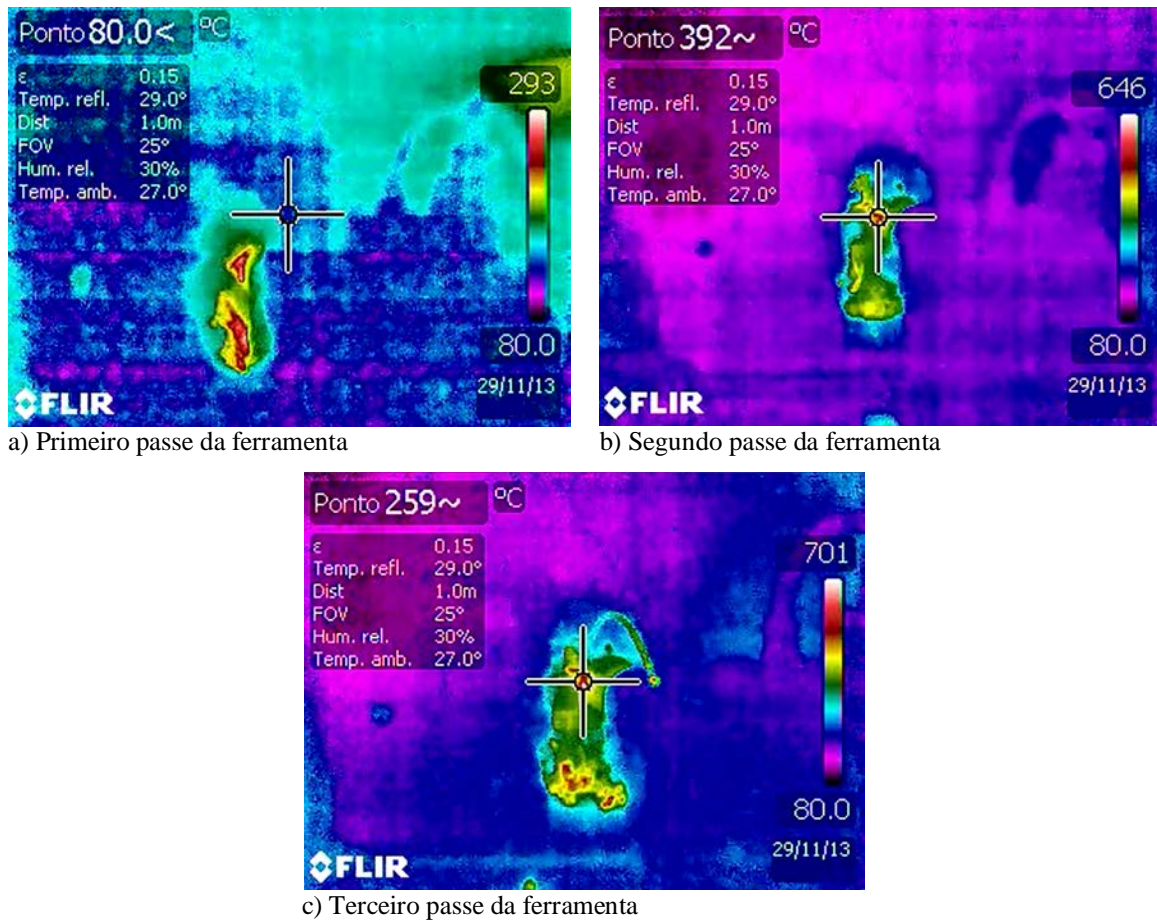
Termografias da usinagem no torneamento do aço ABNT 4340 com velocidade de corte de 150 m/min, avanço de 0,20 mm/rev e profundidade de usinagem de 0,75 mm com ferramenta recoberta com AlCrN.
